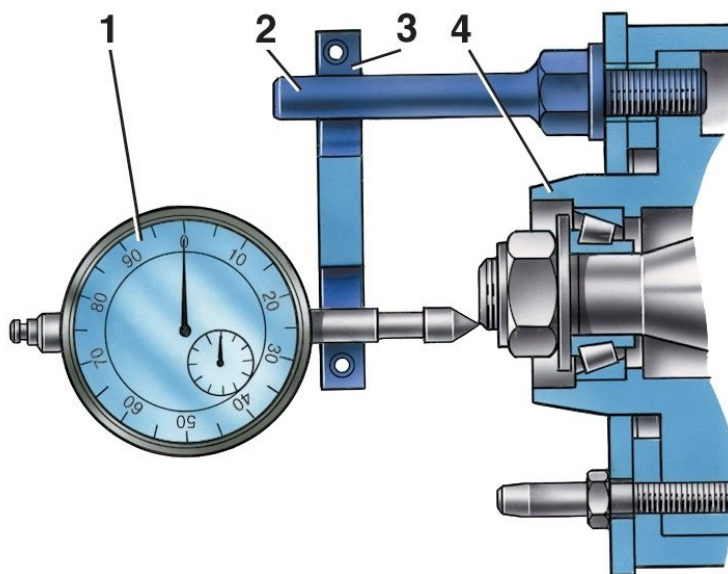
Проверка осевого зазора подшипников ступицы переднего колеса приспособлением 02.7834.9505:
